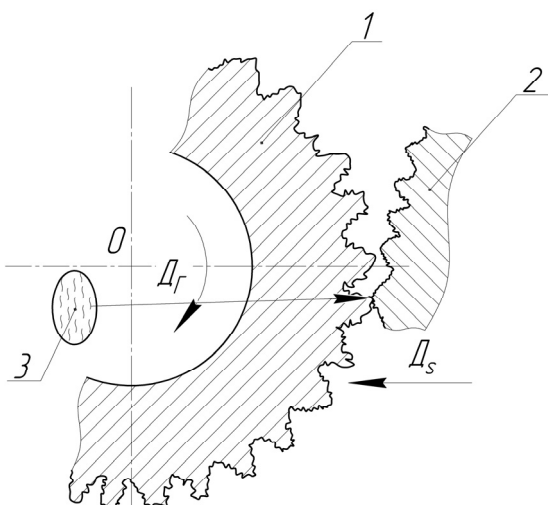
Схема концентрации напряжений, возникающей при силовом скользящем воздействии неровностей режущей кромки на неровности заготовки при точении: 1 – заготовка; 2 – режущая кромка; 3 – микротрещины фреттинга
